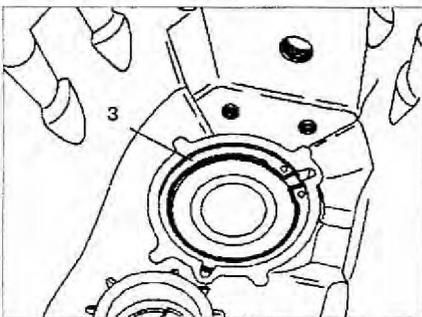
Снимите стопорное кольцо 3 подшипника вторичного вала.
